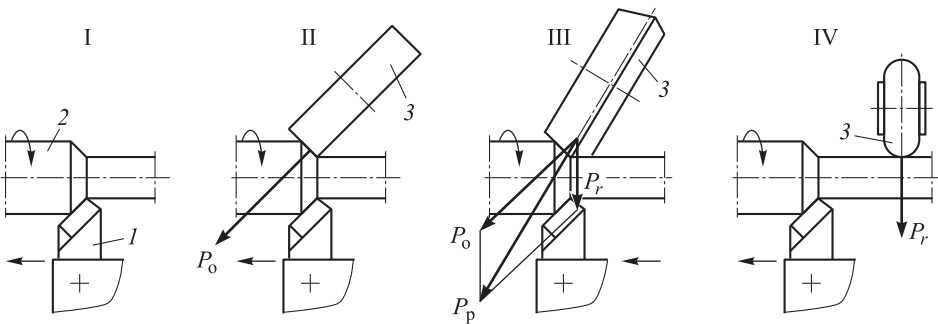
Схемы обработки образцов для исследования шероховатости поверхности (1 — инструмент; 2 — заготовка; 3 — накатной ролик):
